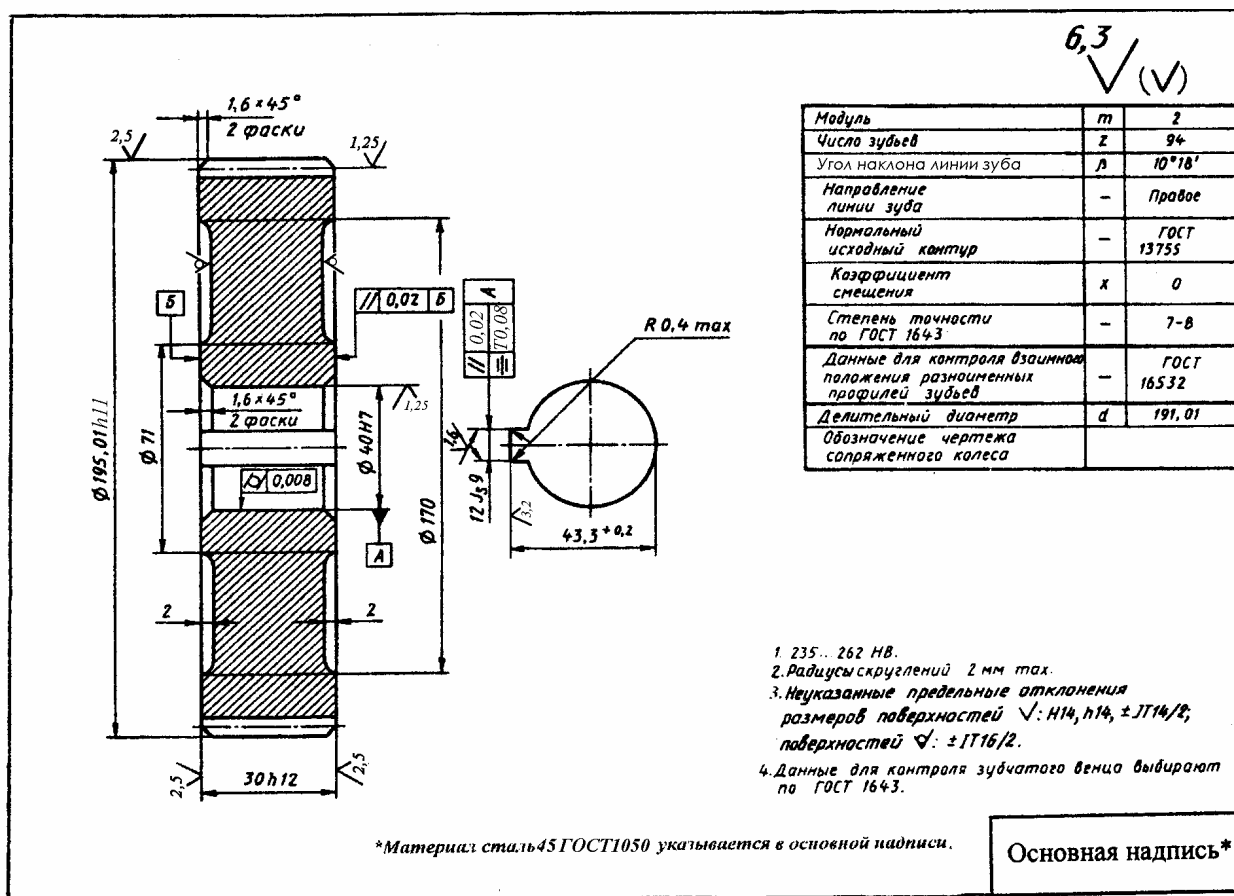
Рабочий чертеж цилиндрического косозубого колеса
